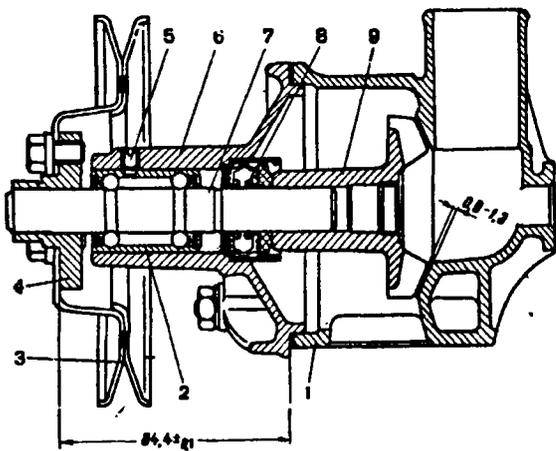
Продольный разрез насоса охлаждающей жидкости: 1 - корпус; 2 - подшипник; 3 - шкив; 4 - ступица шкива; 5 - стопорный винт подшипника; 6 - крышка; 7 - валик; 8 - сальник; 9 - крыльчатка
